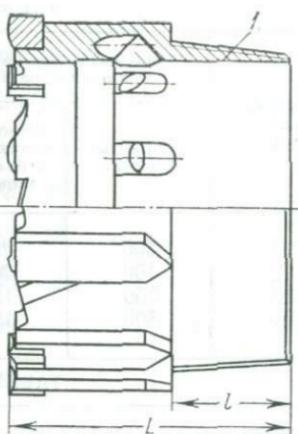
Коронка для пневмоударного бурения типа КДП:
